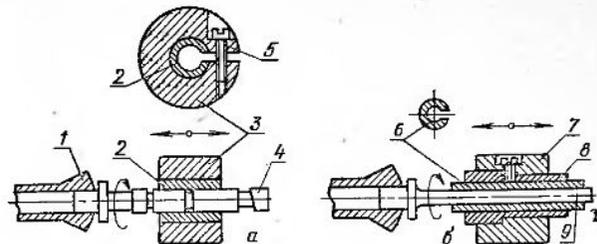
Схема притирки плунжерной пары топливного насоса:
